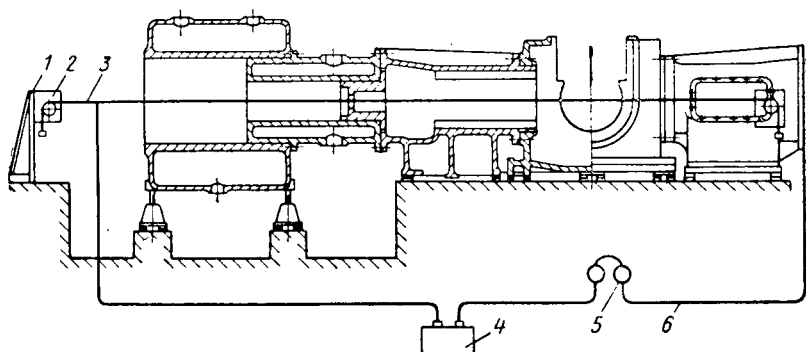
Схема установки струны для центровки цилиндров оппозитного компрессора:
